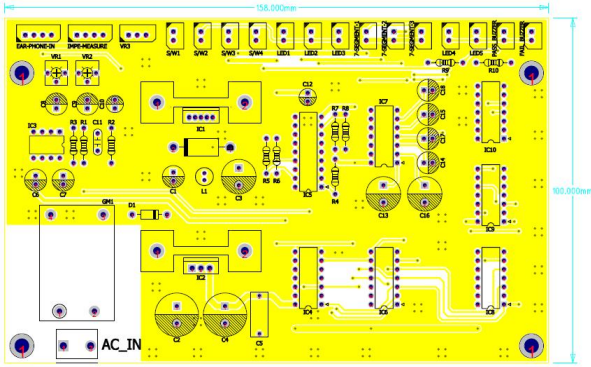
이어폰 기능 검사장치의 메인 PCB 보드
